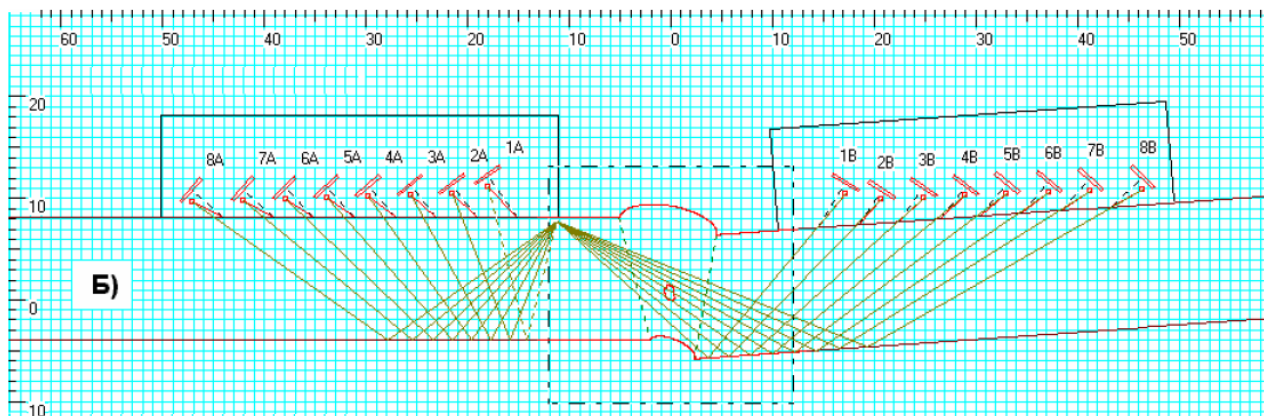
Контроль центральной области сварного соединения
